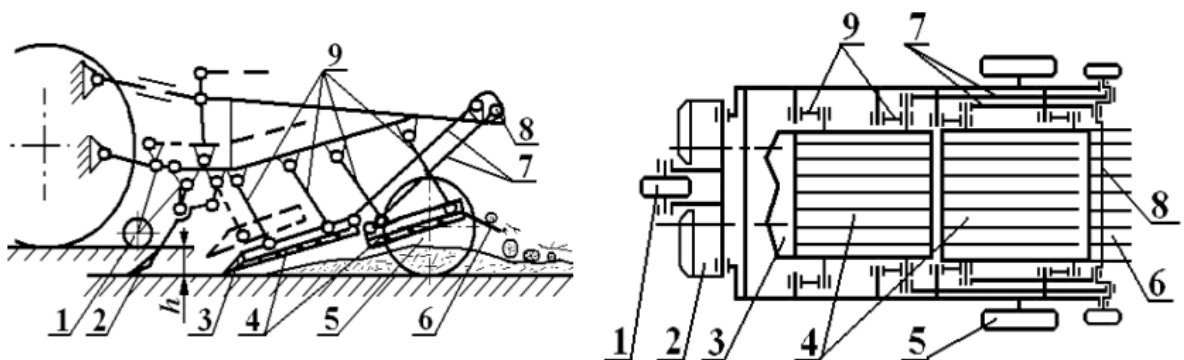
Схема грохотного копача: 1 – опорний коток; 2 – запобіжна напівскоба; 3 – леміш; 4 – дворешітний грохот; 5 – опорне колесо; 6 – струшувальна решітка; 7 – шатуни; 8 – ексцентриковий вал; 9 – підвіски решета.
